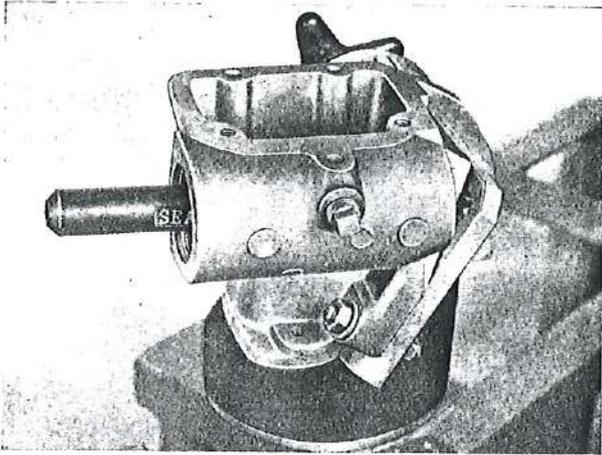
Desmontaje del retén de grasa, mediante el útil A. 10110.
